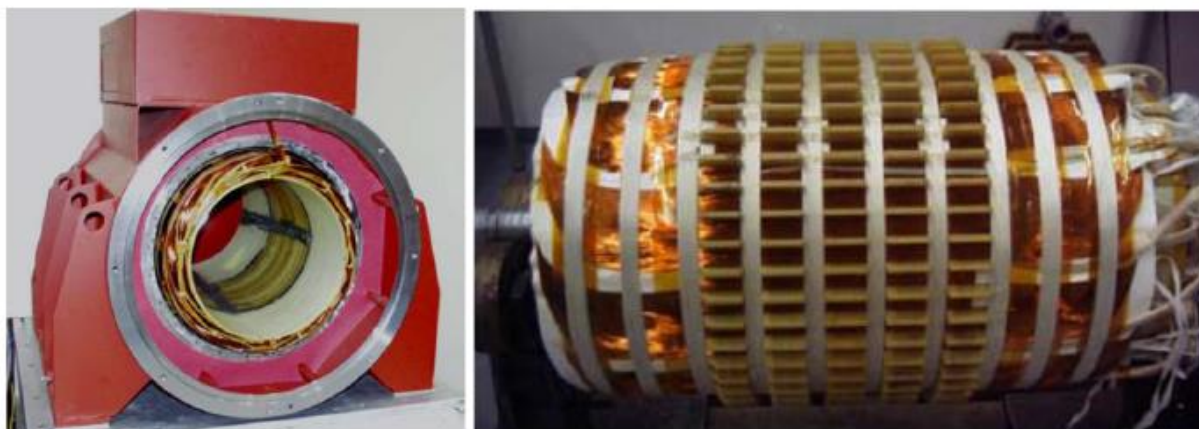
Induit à air de la machine Siemens AG : 400kW-1500 tr/min [19].
